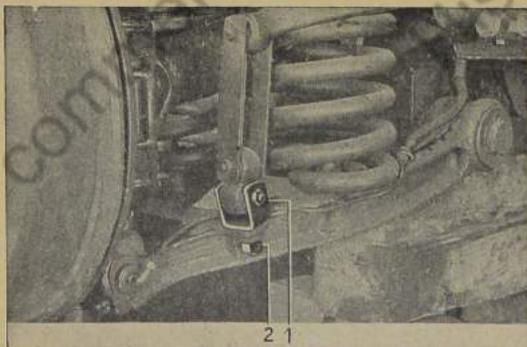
Bügel für Stoßdämpfergelenk abschrauben
